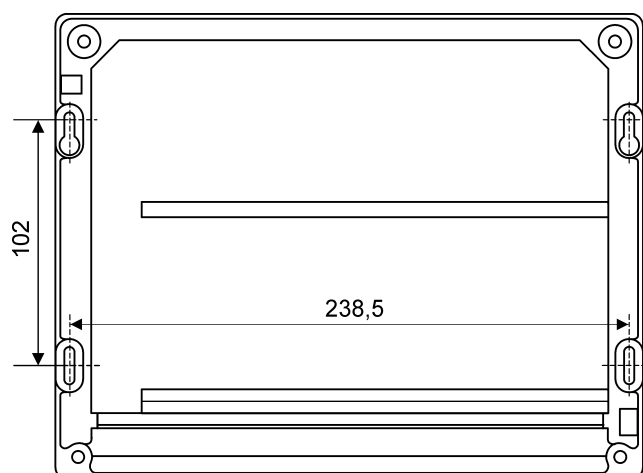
Присоединительные размеры корпуса преобразователя
